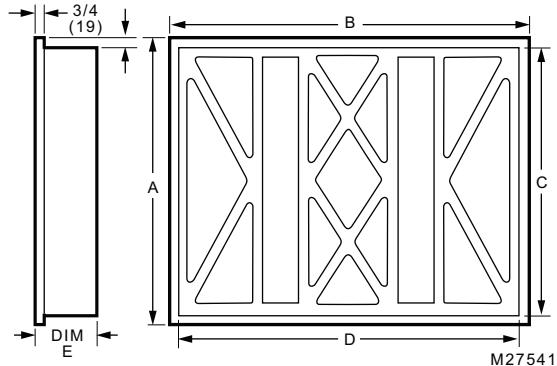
Dimensions en po (mm) (voir le Tableau 1).
